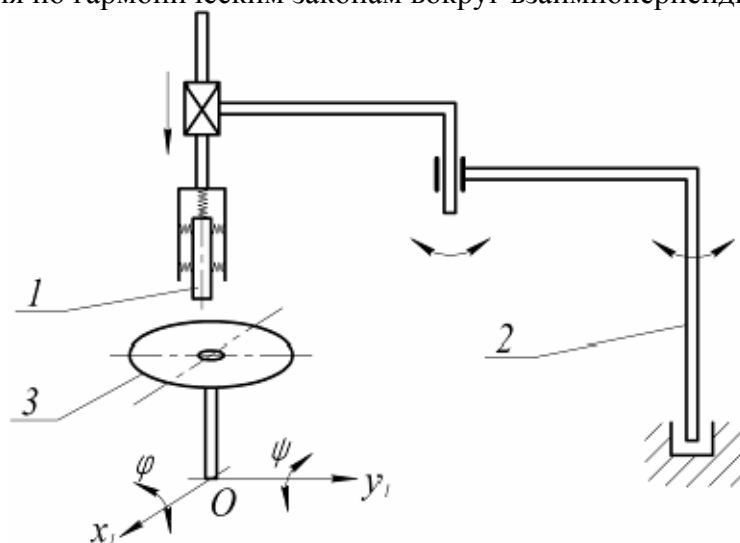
Кинематическая схема метода APC с применением пассивной адаптации и виброколебаниями базовой детали: 1) устанавливаемый вал; 2) промышленный робот; 3) виброопора с установленной в ней базовой деталью
